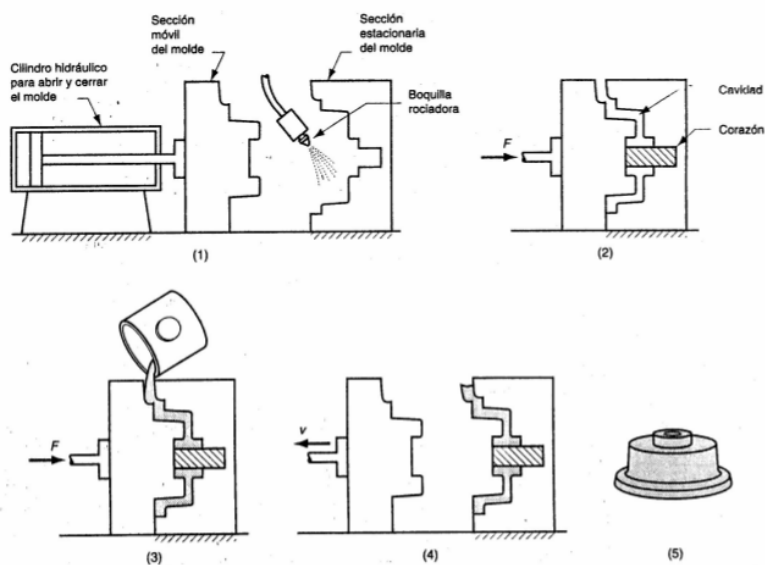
Proceso de fundición en molde permanente: (1) el molde se precalienta y se recubre; (2) Se insertan los corazones, de ser el caso y se cierra el molde; (3) el metal fundido se vacía en el molde; (4) se abre el molde y (5) pieza terminada <sup>48</sup>
